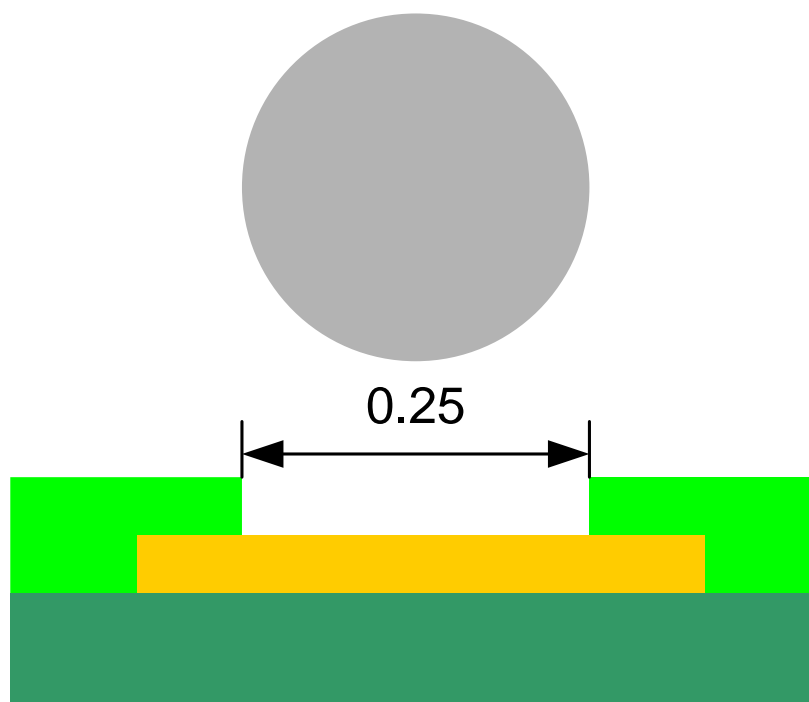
Конструкція посадкового місця BGA-кульки
